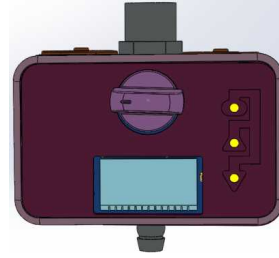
PCB가 실장된 내부 기구설계 부품 조립도
